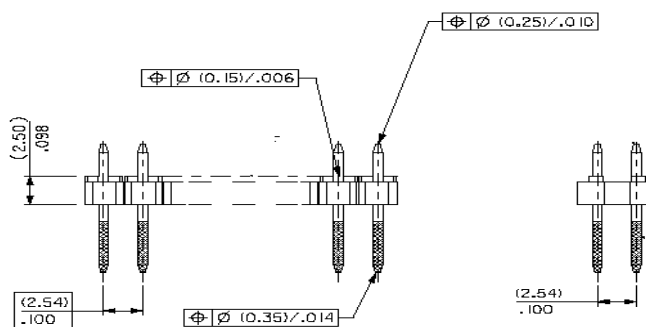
Габарити з'єднувача 90120-0766
